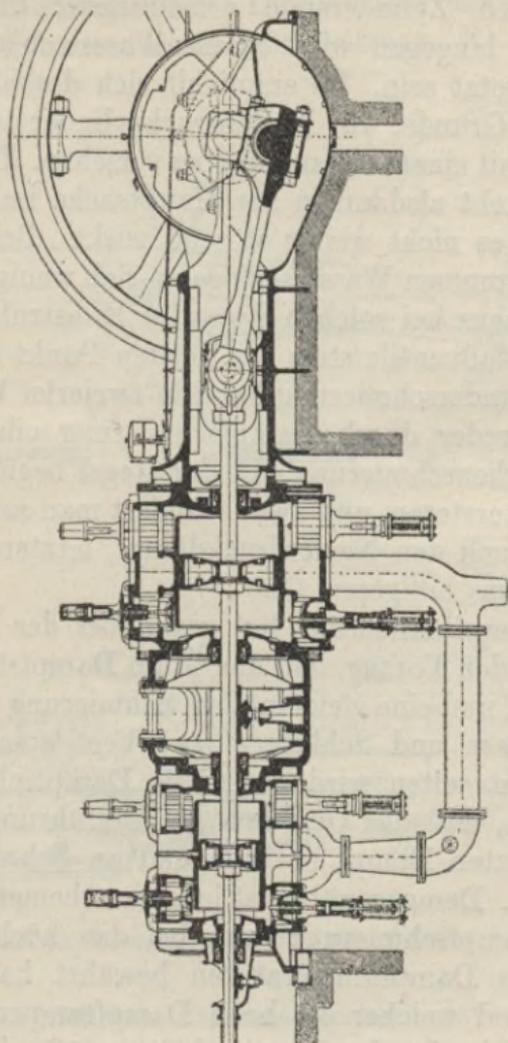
M.A.N.-Heißdampf-Tandemmaschine mit Lentz-Steuerung.
